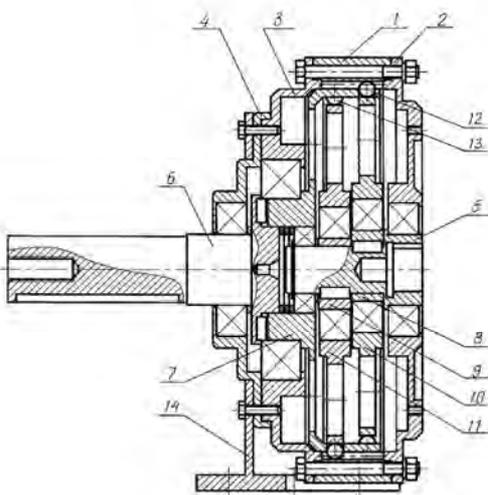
Редуктор привода станка для монтажа автомобильных шин
